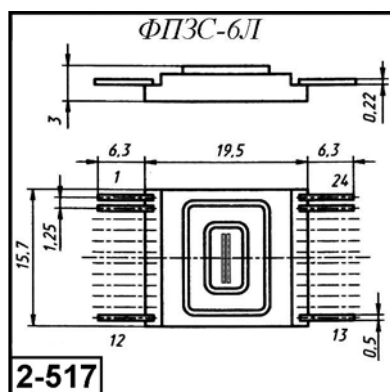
Внешний вид и габаритные размеры ФПЗС-6Л
